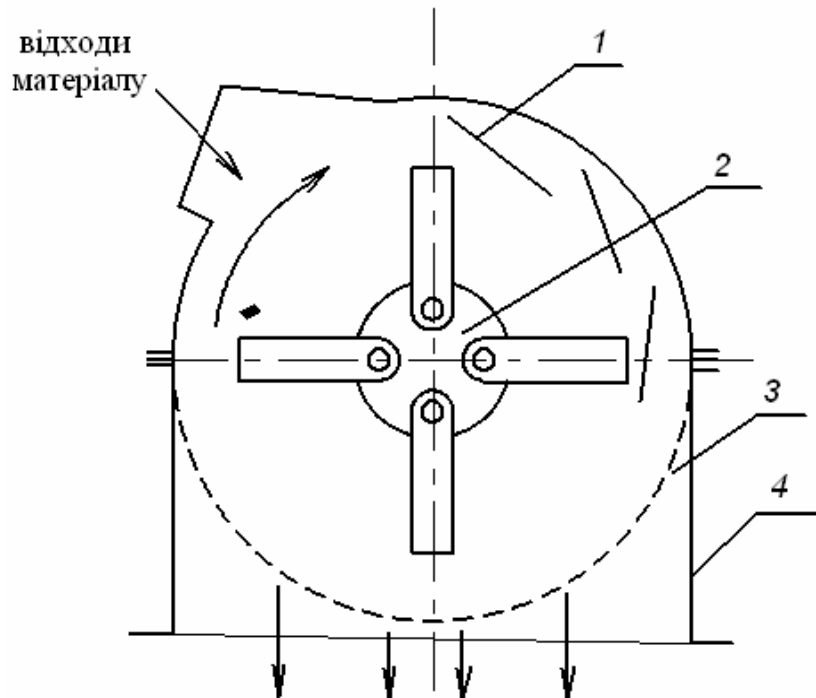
Молотковий подрібнювач: 1 – відбивні рифлі; 2 – молотковий ротор; 3 – решітка; 4 – корпус
